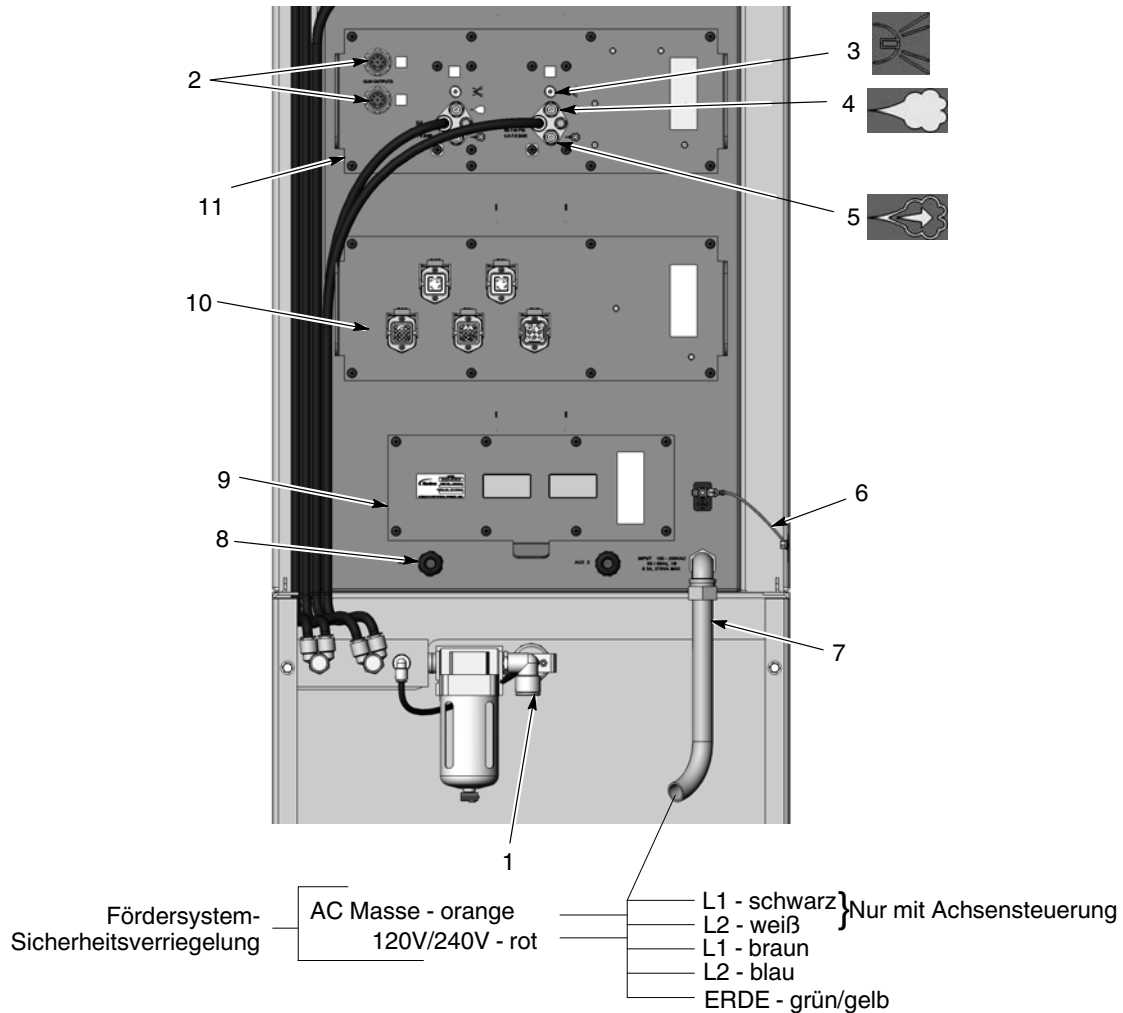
Steuerung für mehrere Pistolen - Anschlüsse für Netz, Luft und Pistolen (rückseitige Abdeckung und Schutzplatte abgenommen)
